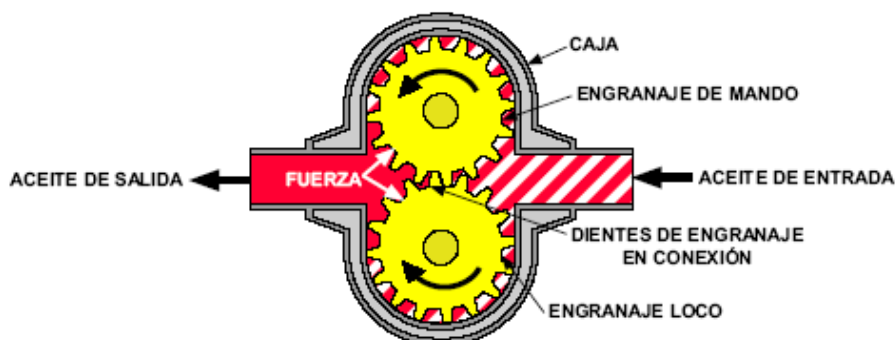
Fuerzas en la bomba de engranajes
